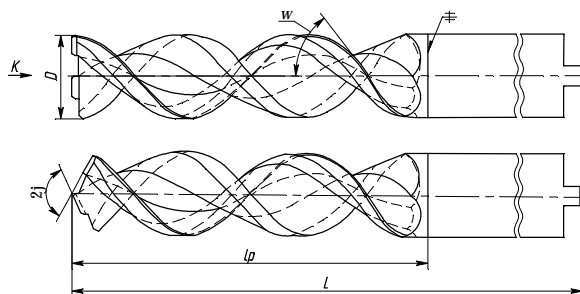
Бессердцевинное спиральное сверло «Зигзаг» без поперечной кромки
